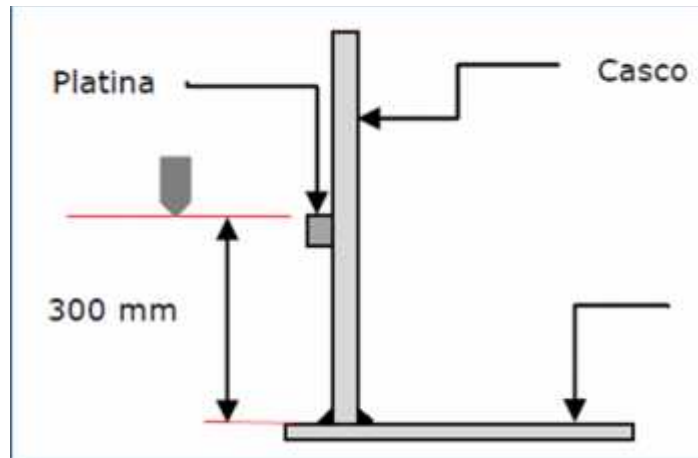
Esquema de medición con platina testigo soldada.
